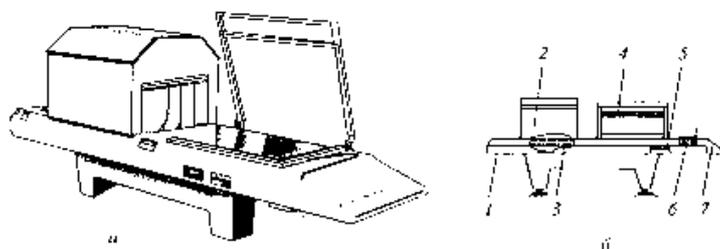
Упаковочный аппарат ТПЦ-370: а - общий вид; б - контурная схема; 1 - сборный металлический корпус; 2 - термокамера; 3 - металлический конвейер; 4 - рамный импульсный термонож; 5 - пульт управления; 6 - рассекатель «полурукава» термоусадочной пленки; 7 - валы для установки бобины с пленкой
